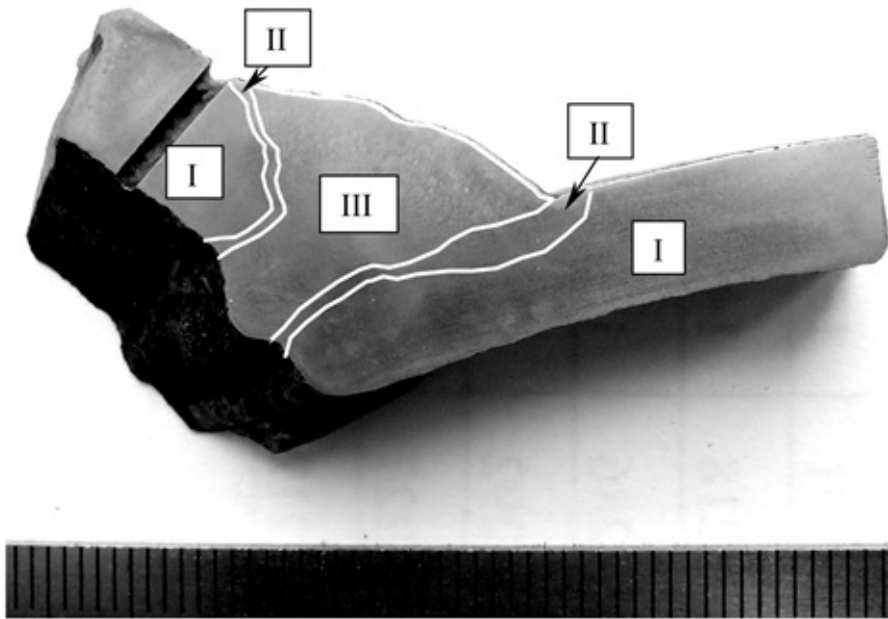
Темплет №1 с обозначением границ сварного шва (после травления):
